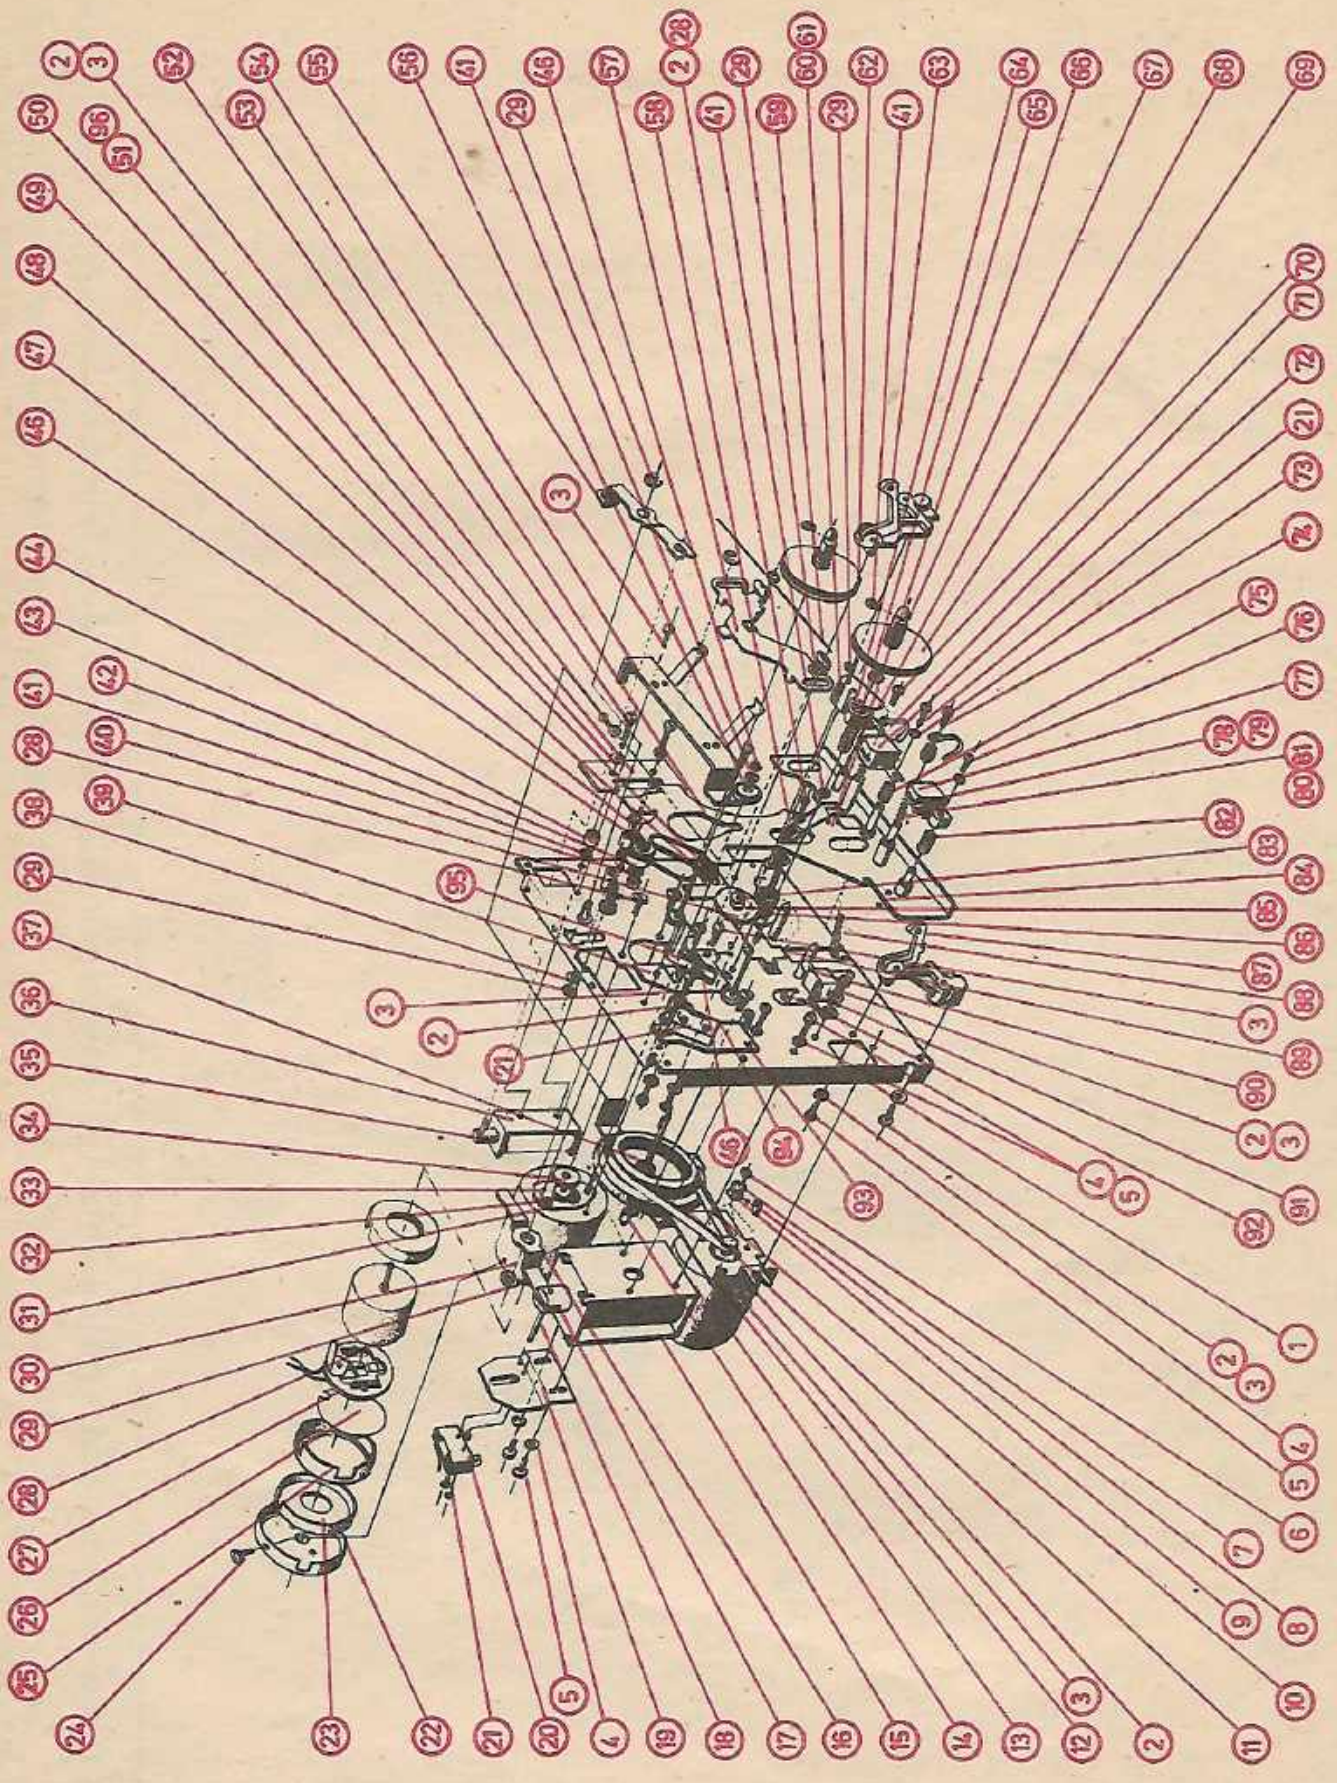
Rozmieszczenie i widok ogólny elementów mechanicznych magnetometru MDS-411D
